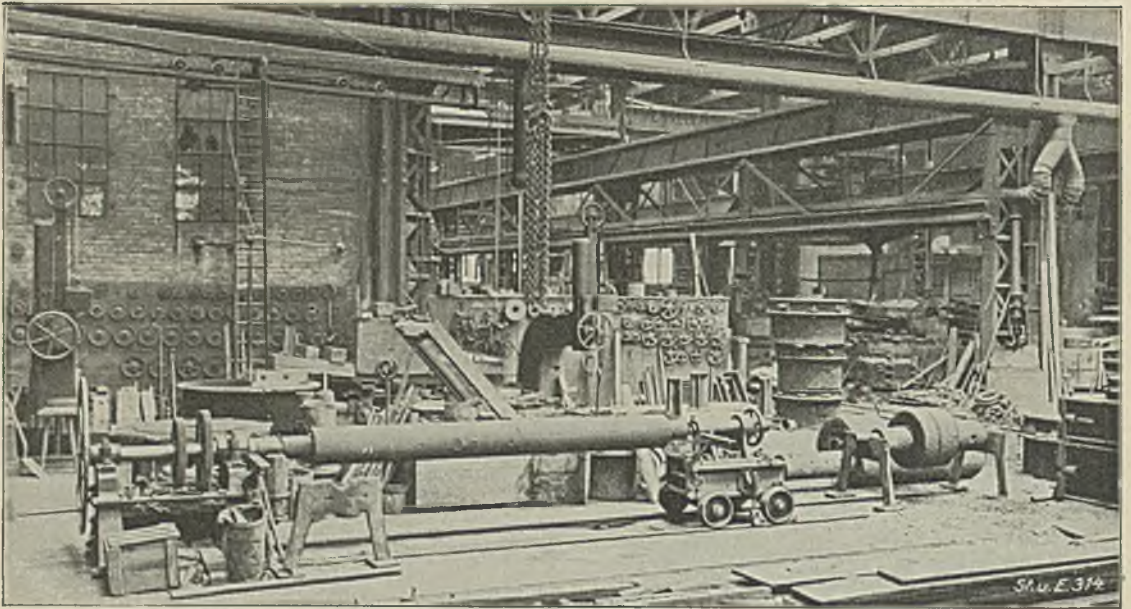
Kerndrehbank und Räderformmaschinen.
